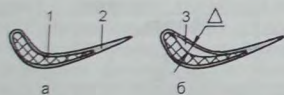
Схемы разрезов моделей пера турбинных лопаток: 1 — керамический стержень; 2 — модель отливки; 3 — воздушный зазор
